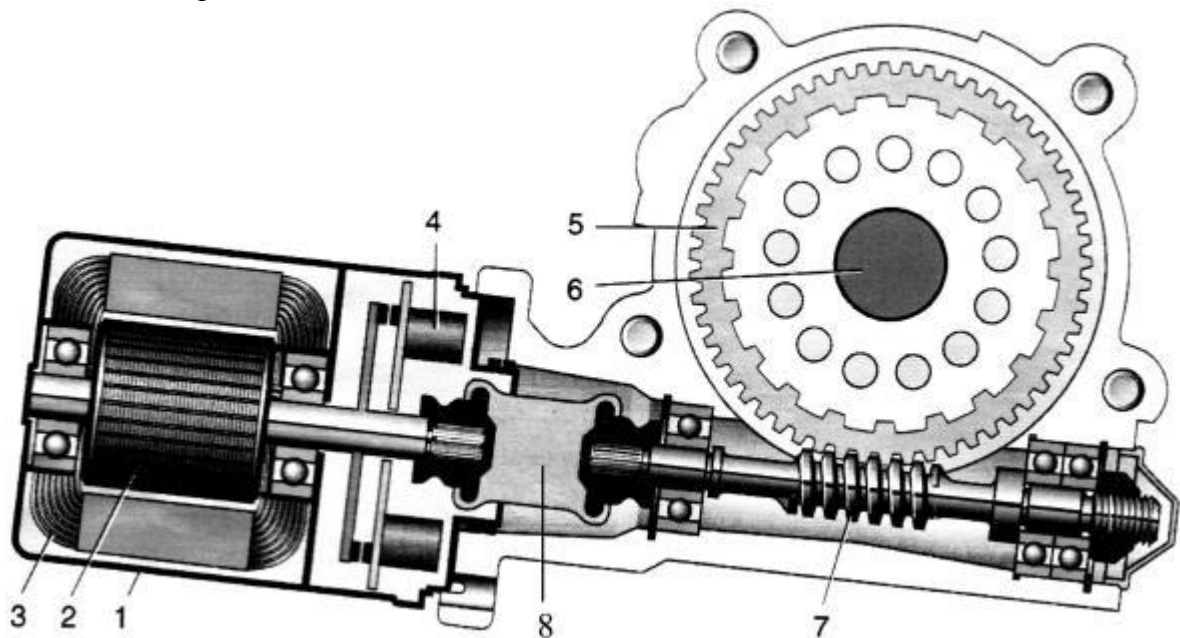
Розріз електропідсилювача рульового керування: 1 – трифазний синхронний електродвигун; 2 – якор; 3 – обмотка статора; 4 – датчик положення якоря; 5 – черв'ячне колесо; 6 – рульовий вал; 7 – черв'як.
